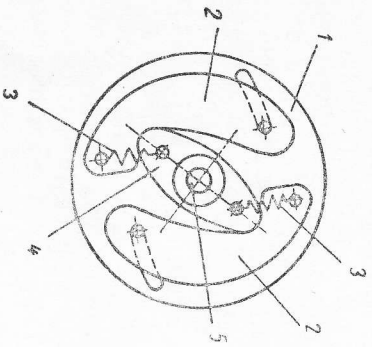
Центробежный регулятор опережения зажигания: 1 — основание, соединенное с приводным валиком; 2 — подвижные грузы; 3 — пружины; 4 — фланец; 5 — валик, соединенный с кулачком прерывателя.
